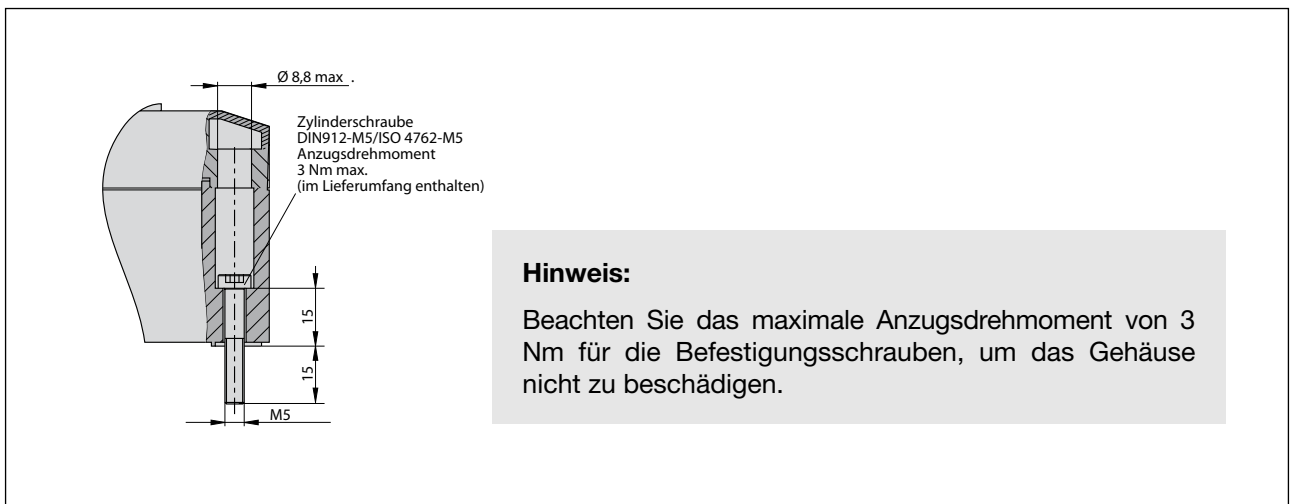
Befestigungsschrauben (Teil des Lieferumfangs)
